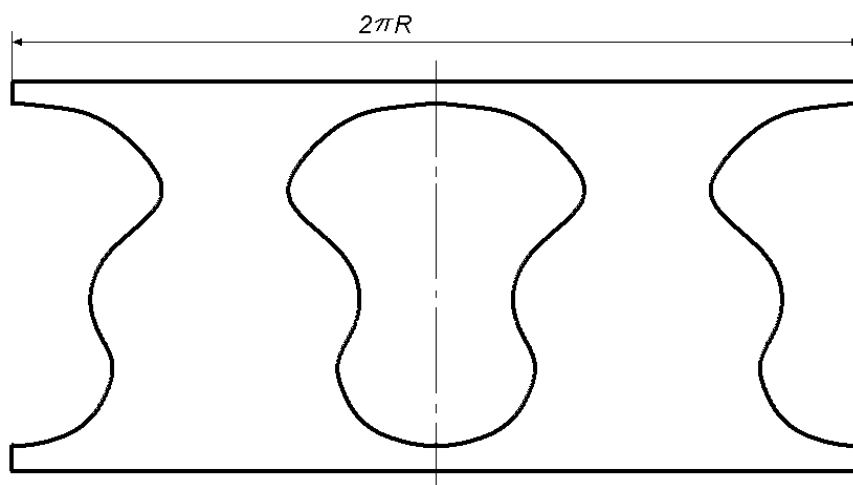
Розгортка бічної поверхні циліндра із контуром наскрізного отвору, форма якого представлена на рис. 5.39,б
